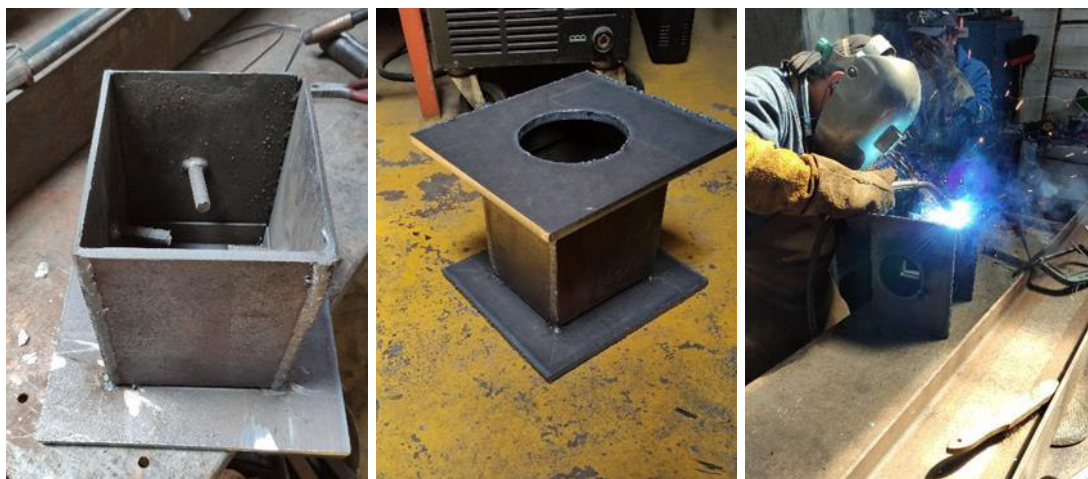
Soldadura de diafragmas de conexión viga-columna.
